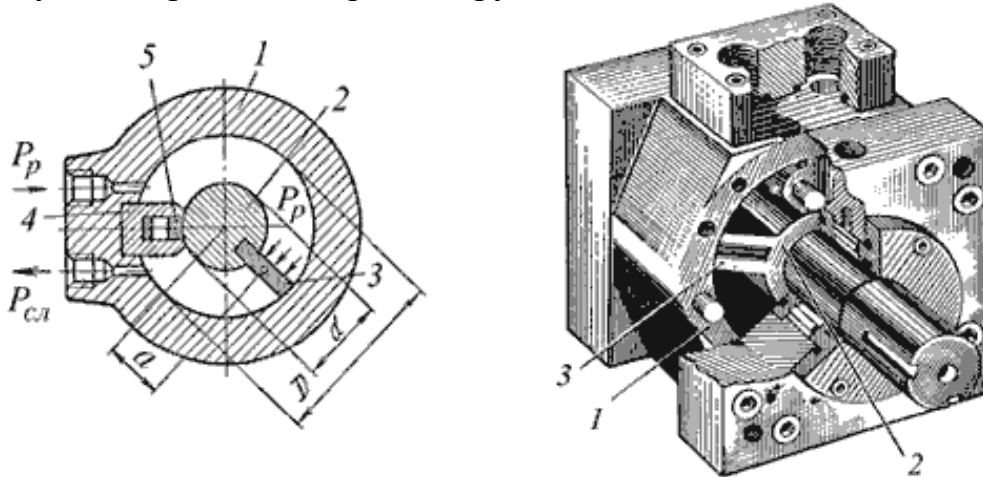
Поворотний однолопатний гідроциліндр: а - схема; б - загальний вигляд
